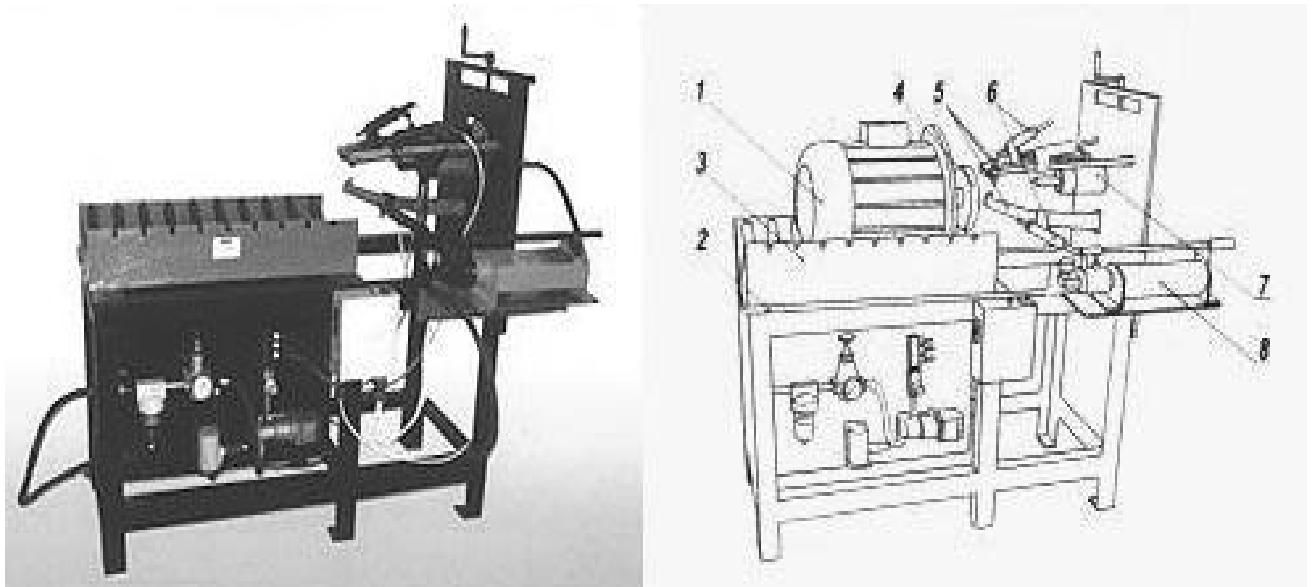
Установа запресування підшипників УВП-901А.
